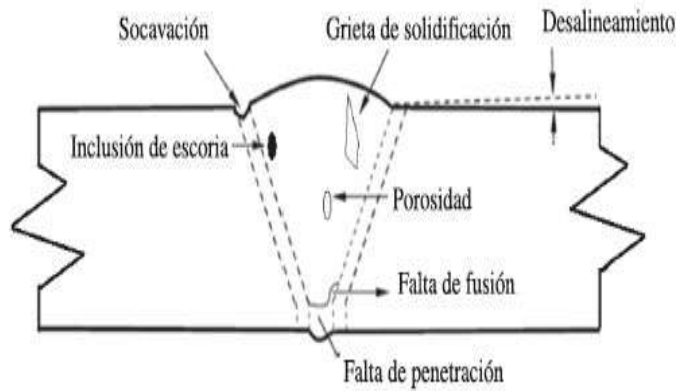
Imperfecciones de soldadura en juntas a tope. Fuente: Barsom (1994).
